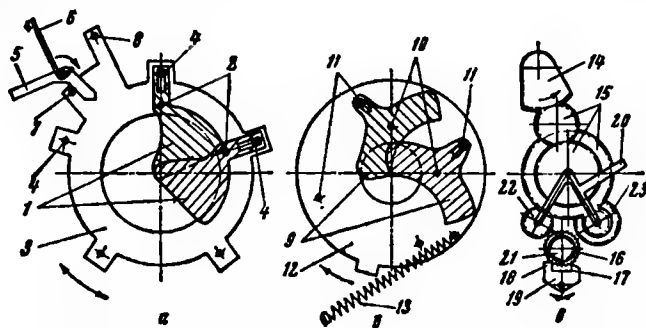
Схемы привода лепестков и анкерного регулятора центральных фотошutters:
